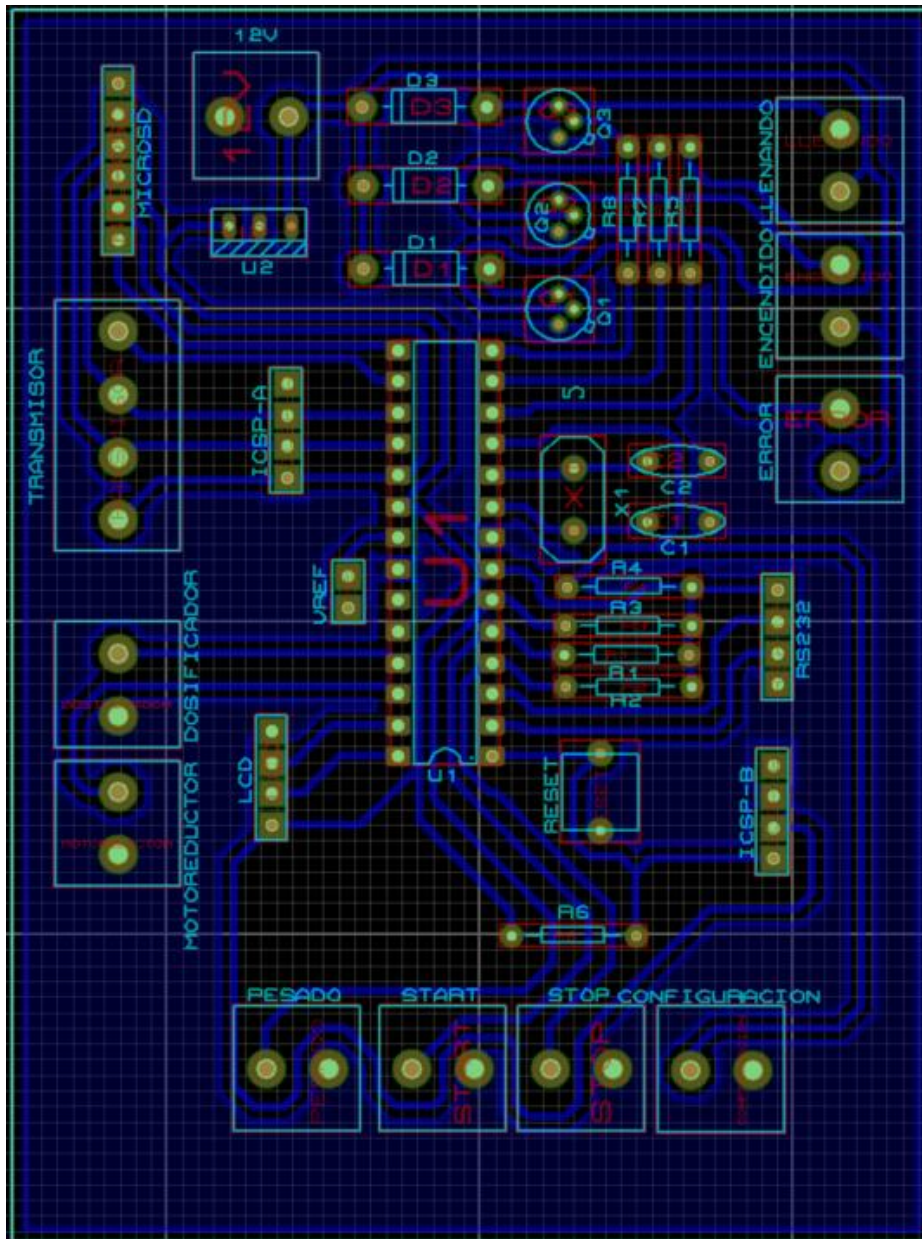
PCB diseñada para microcontrolador (Fuente Propia, 2023)
